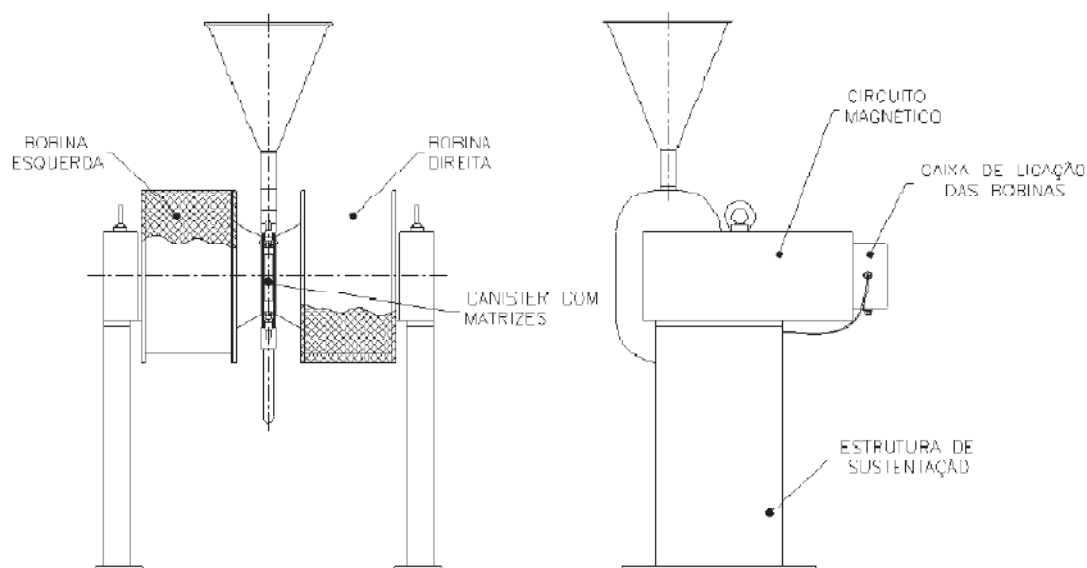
Concentrador Eletromagnético de Carrossel mod. L-4, fabricado pela INBRAS. À esquerda, vista frontal e à direita, vista lateral
